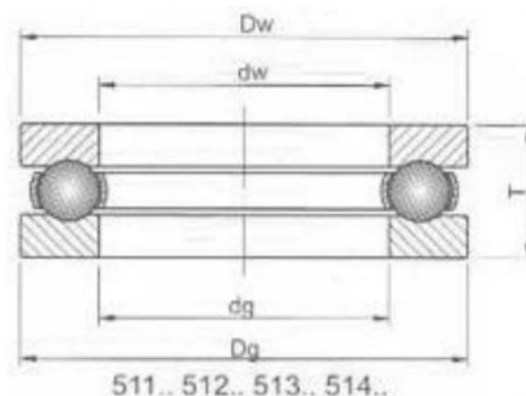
Схема обозначений размеров упорного подшипника.
